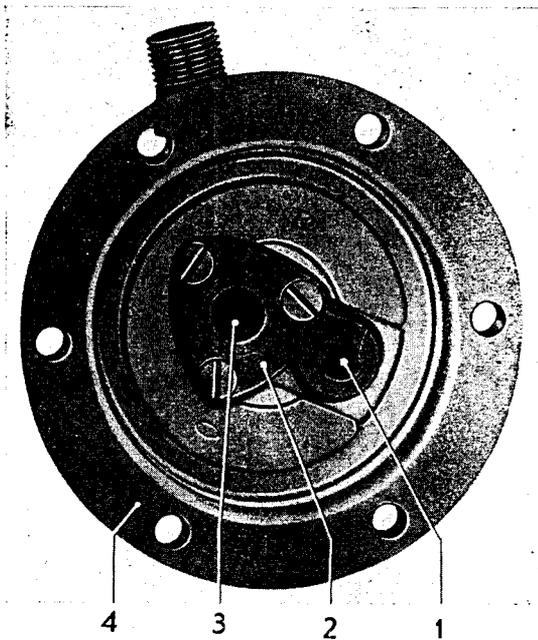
Ventil Sitzplatte im Gehäuseoberteil abschrauben
